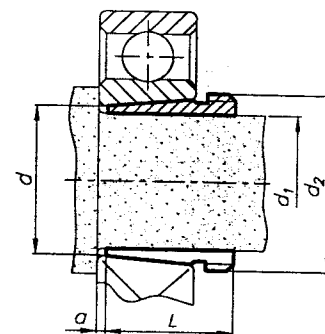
Закрепление внутреннего кольца подшипника на валу с использованием стяжной втулки
